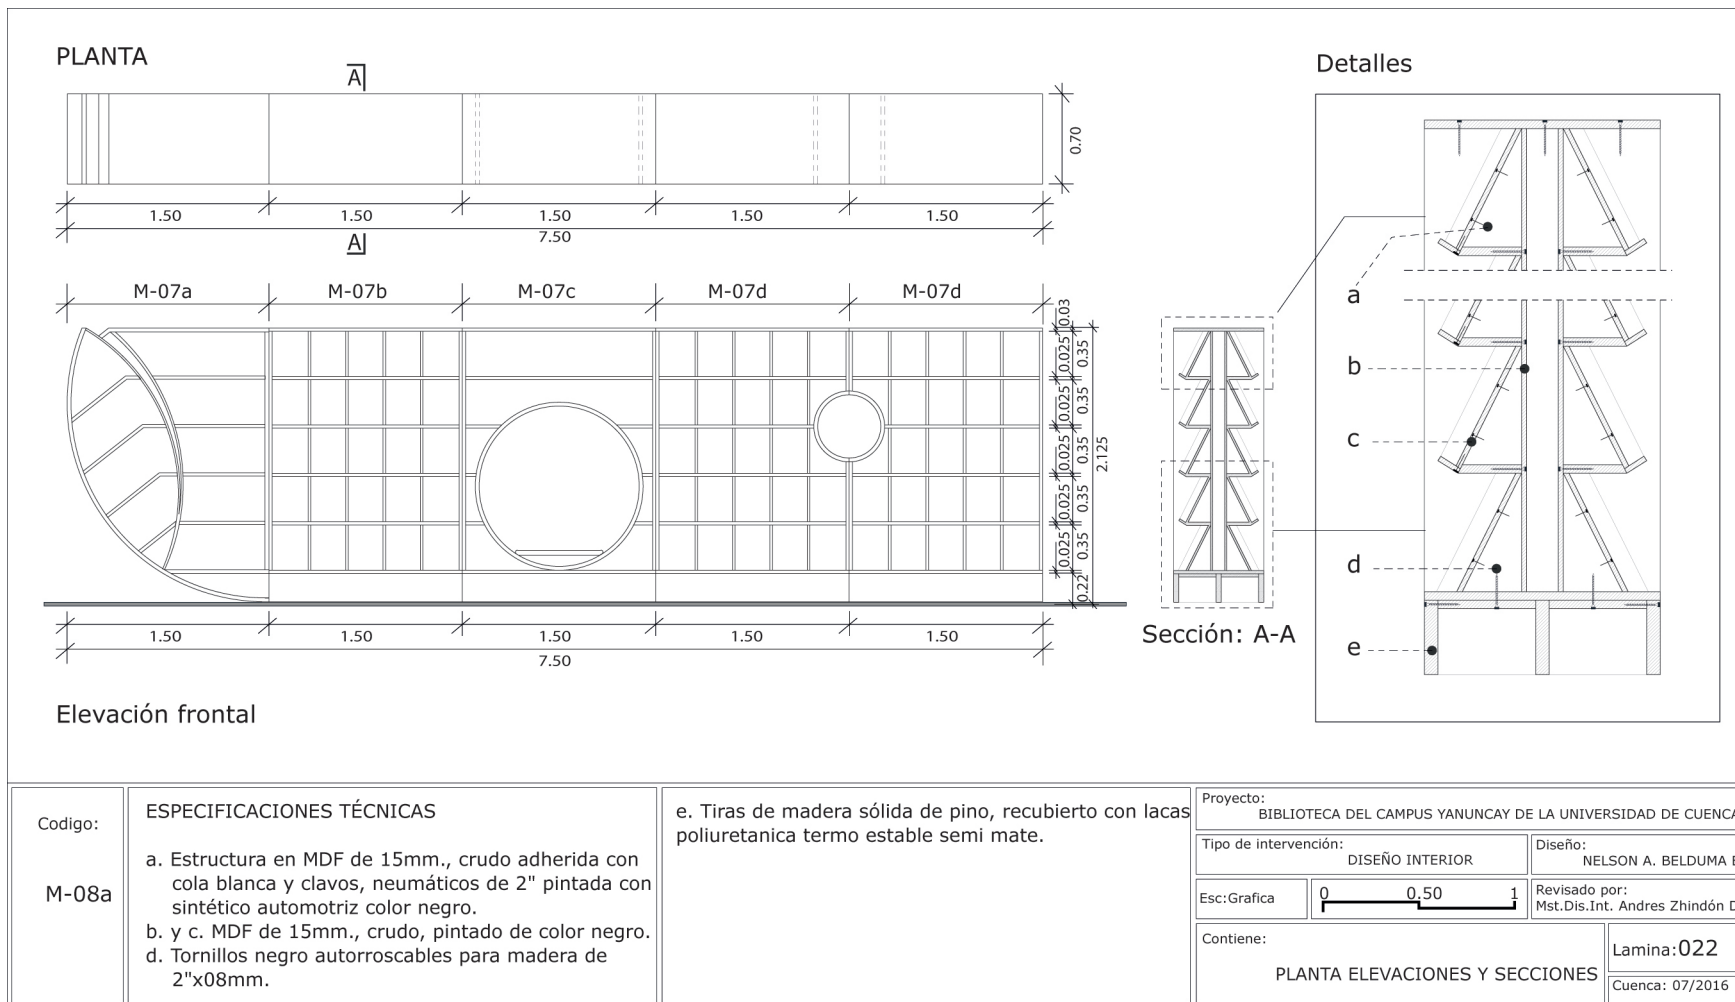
Planta de elevaciones y secciones. Estanterías. M-08a.
